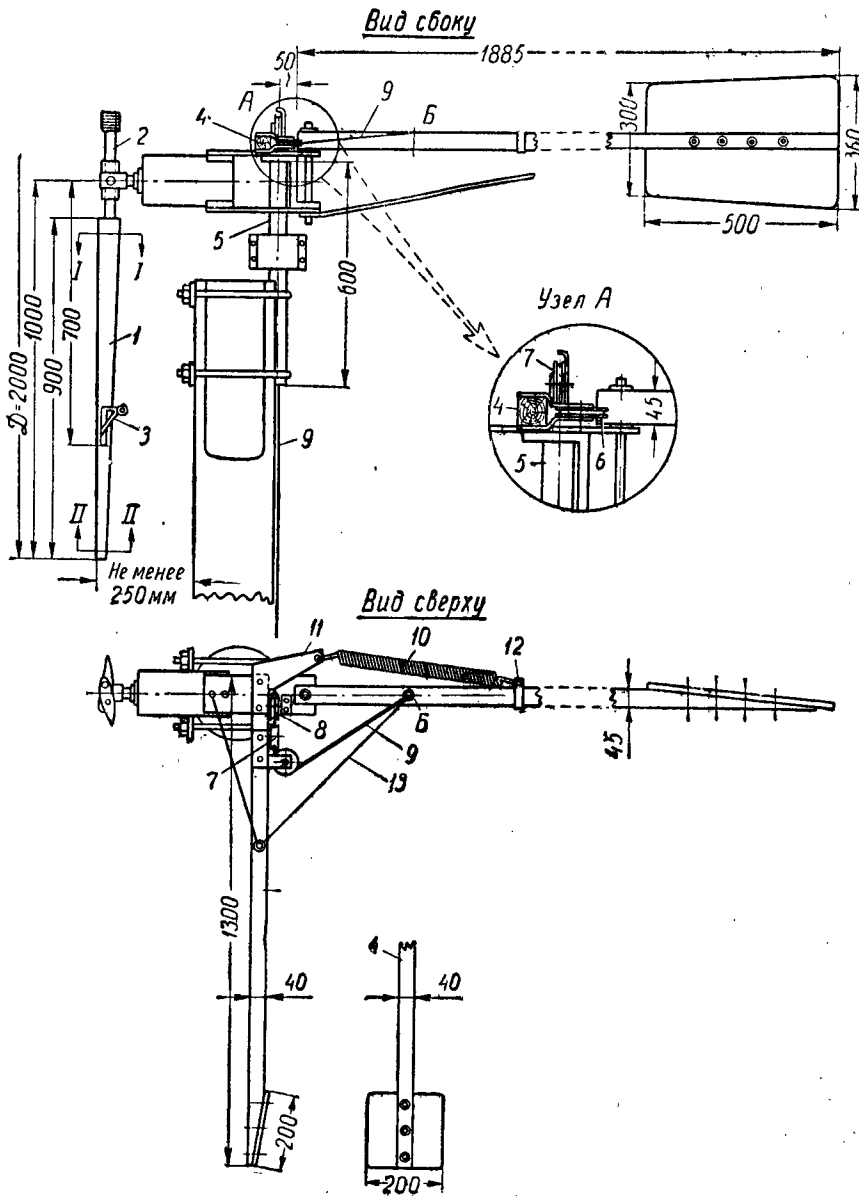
Ветродвижитель с однолопастным ветроколесом: 1 — лопасть; 2 — стержень противовеса; 3 — клапан регулятора оборотов; 4 — стержень боковой лопасти; 5 — опорная труба; 6, 7, 8 — ролики троса останова; 9 — трос останова; 10 — пружина хвостовая; 11 — кронштейн крепления пружины к головке; 12 — обойма крепления пружины к хвостовому стержню; 13 — тяга упорная
